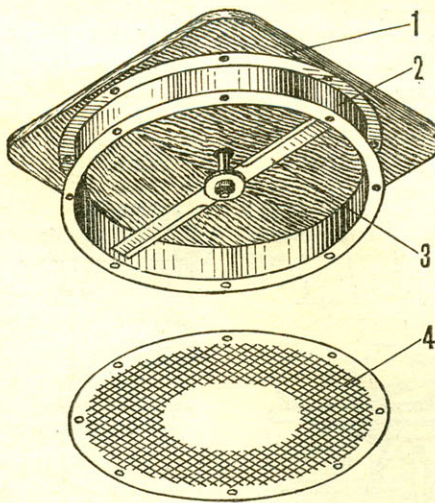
Дробильная камера (вид снизу): 1 — основание, 2 — корпус рабочей камеры, 3 — нож-пластина, 4 — сетка.
